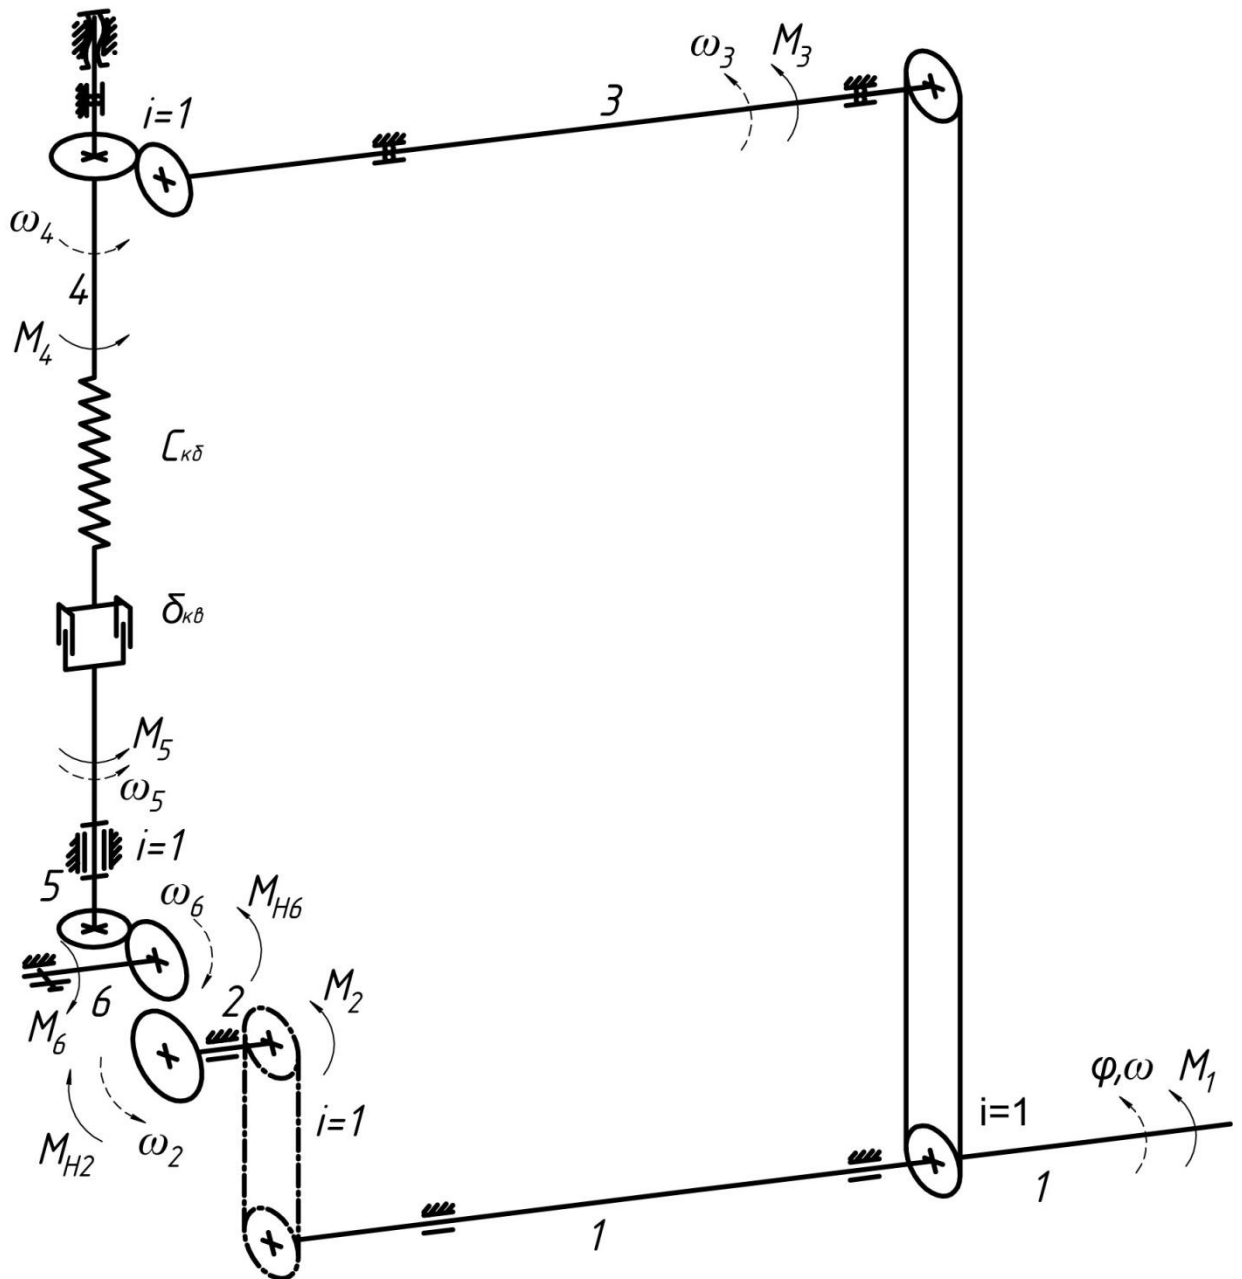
Розрахункова схема механізму транспортування швейної колонкової машини
